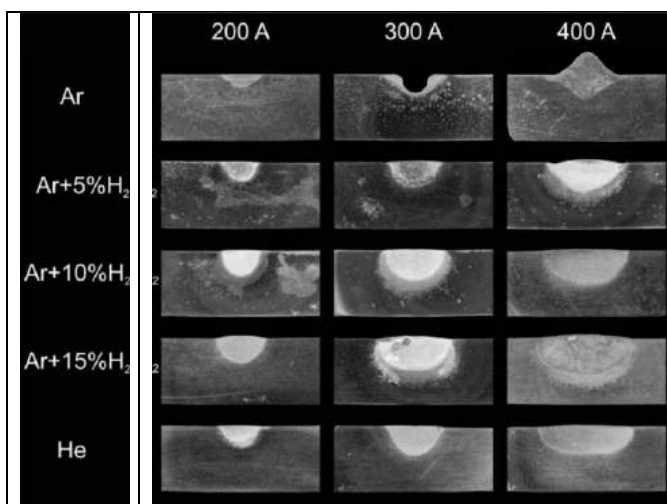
Seções transversais dos cordões cortados a 100 mm do início da soldagem (Schwedersky (1), 2011.)
